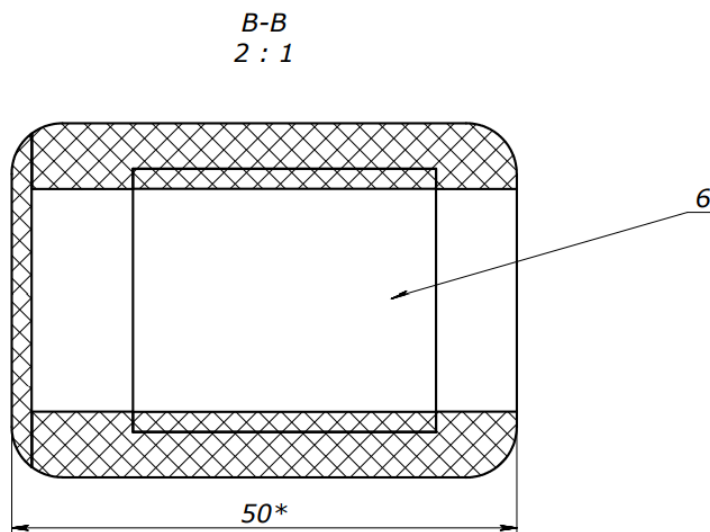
Вид зверху корпусу для датчика
